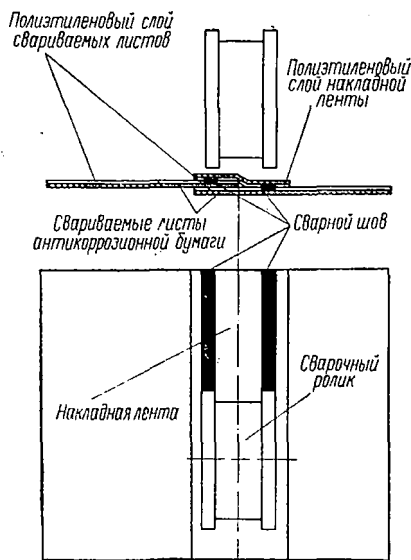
Схема сварки антикоррозийной бумаги
